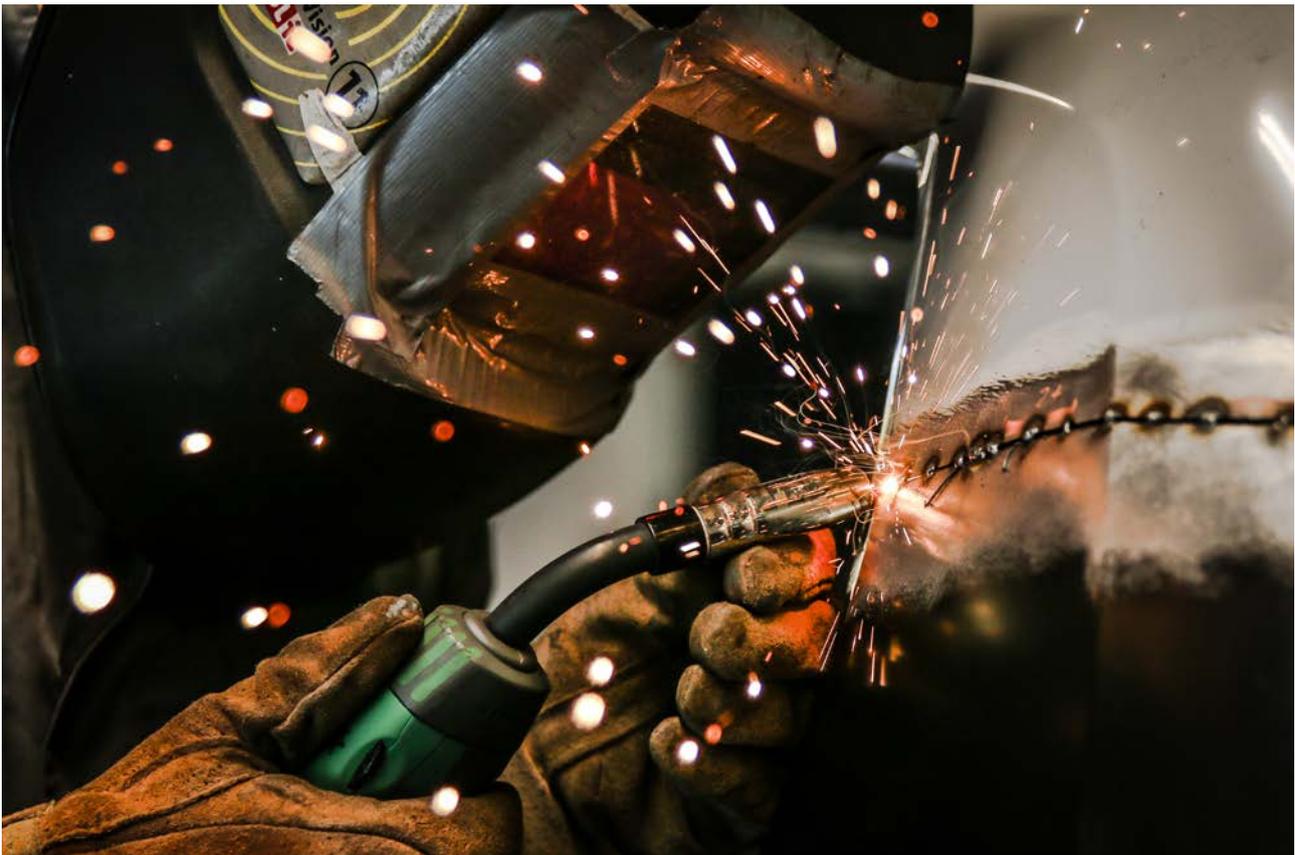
Fügen einer Abschnittsreparatur mit einer MAG-Schweißnaht (Quelle: ZKF)
